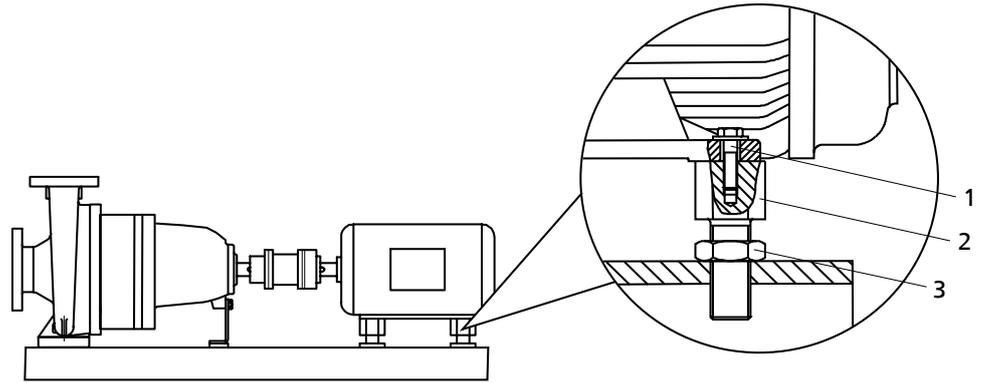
Pumpenaggregat mit Stellschrauben ausrichten
